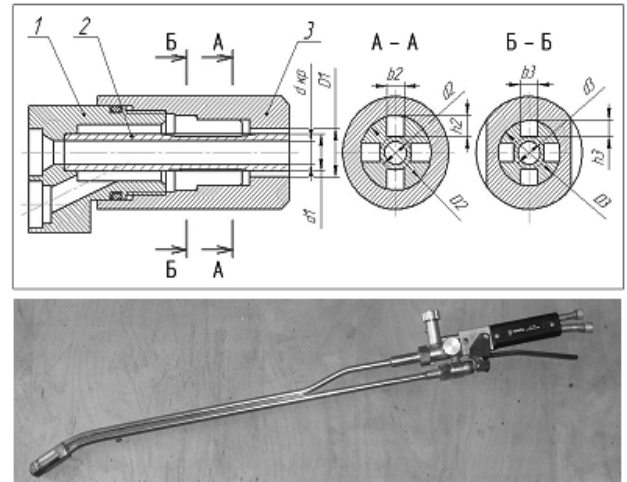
Модуль 6.4. Головка в сборе резака для кислородной резки крупного лома и прибылей литья толщиной до 600 мм – сверху; общий вид резака Р6-ФЛЦ – внизу
